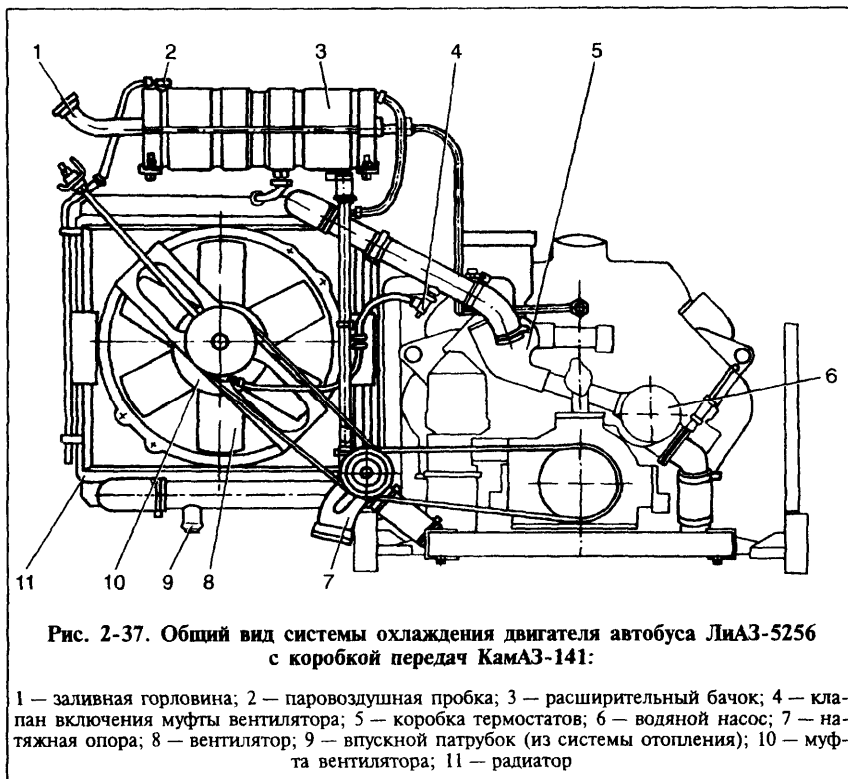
Общий вид системы охлаждения двигателя автобуса ЛиАЗ-5256 с коробкой передач КамАЗ-141:
